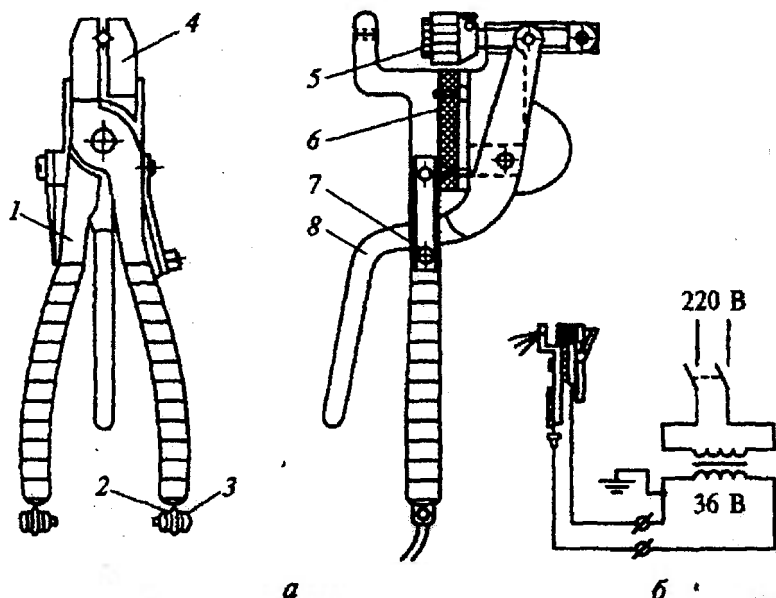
Клещи для сварки проводов:
